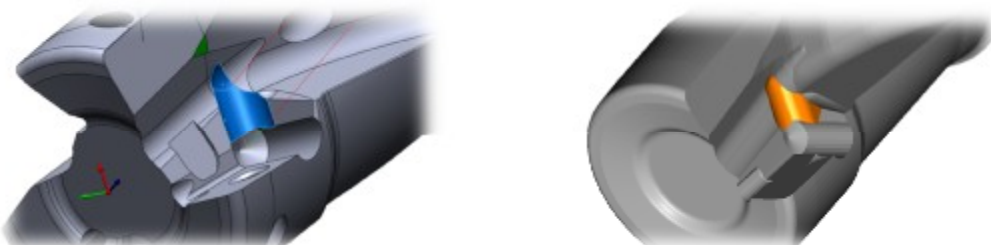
Operace 11 – vygenerované dráhy a obrobení
